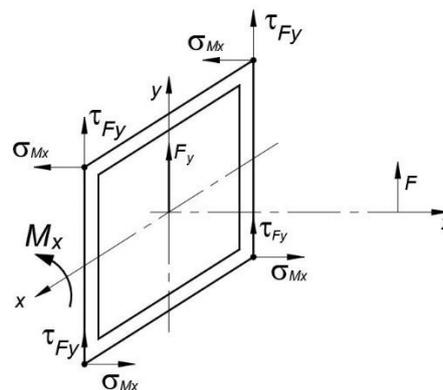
Расчетная схема для сварного шва для варианта 1.
